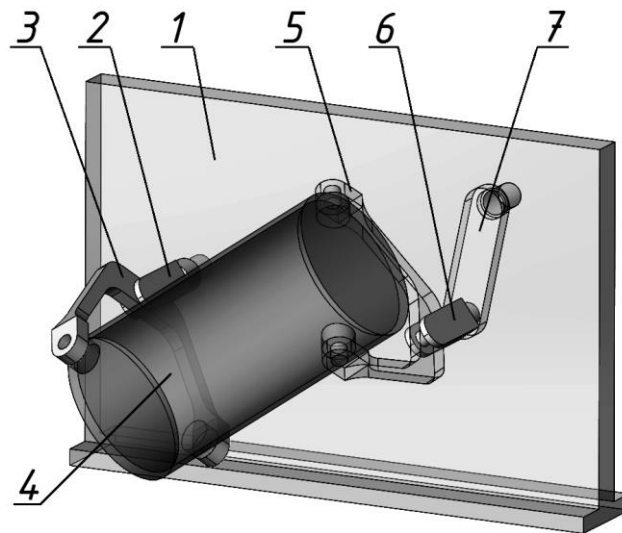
Модель конструкції машини з додатковою рухомою ланкою – коромислом, що має горизонтальну вісь обертання, де 1 – станина, 2 – ведучий вал, 3 – ведуча вилка, 4 – робоча ємкість, 5 – ведена вилка, 6 – ведений вал, 7 – коромисло.
